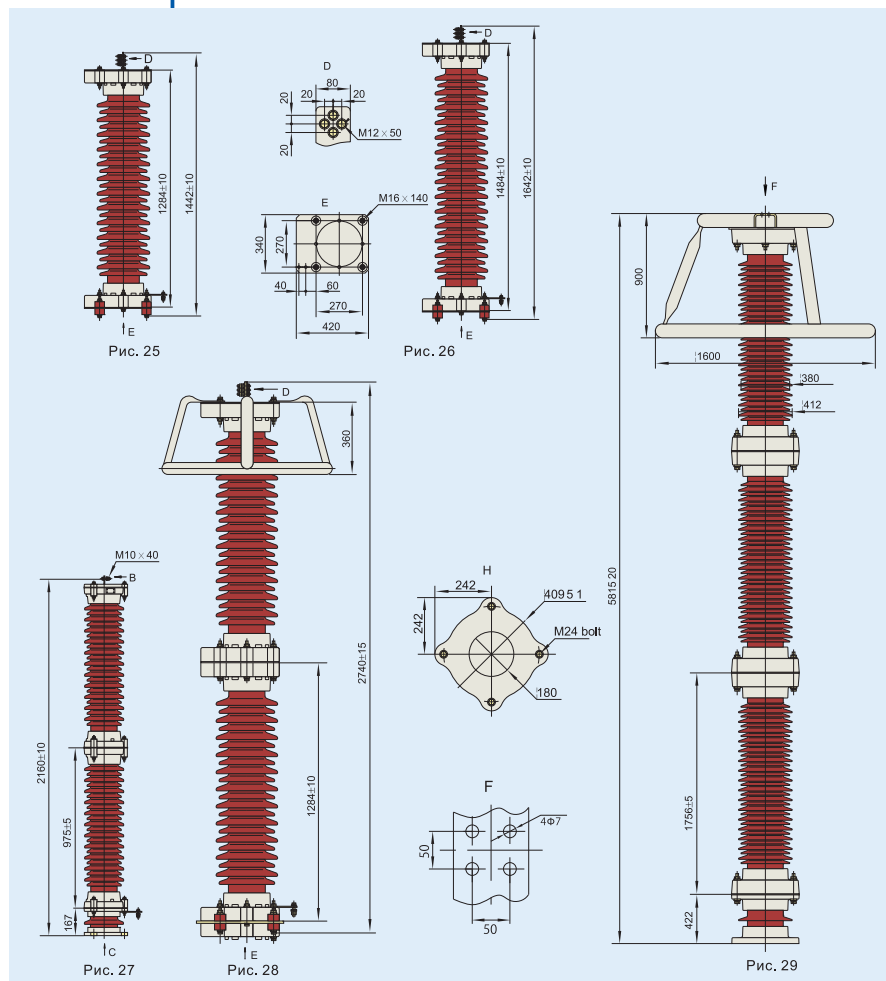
Внешний вид и размеры металлооксидного ОПН
